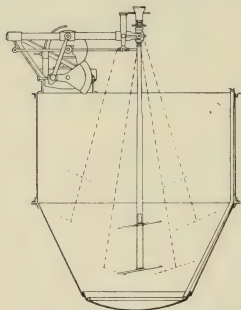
Seifensiedekessel für Dampfsiederei mit Krückwerk.
